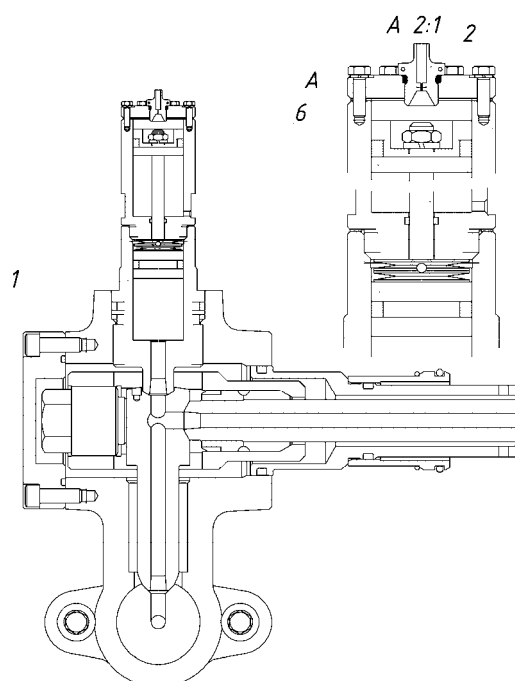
Модернизированный топливопровод двигателя MaK M43
